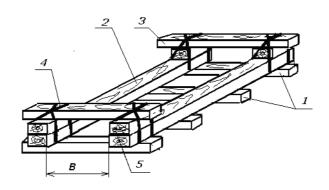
Поддон для упакованных рулонов 1 – поперечный брусок-подкладка; 2 – продольный опорный брусок; 3 – торцевой упорный брусок; 4 – стяжка; 5 – подкладка
